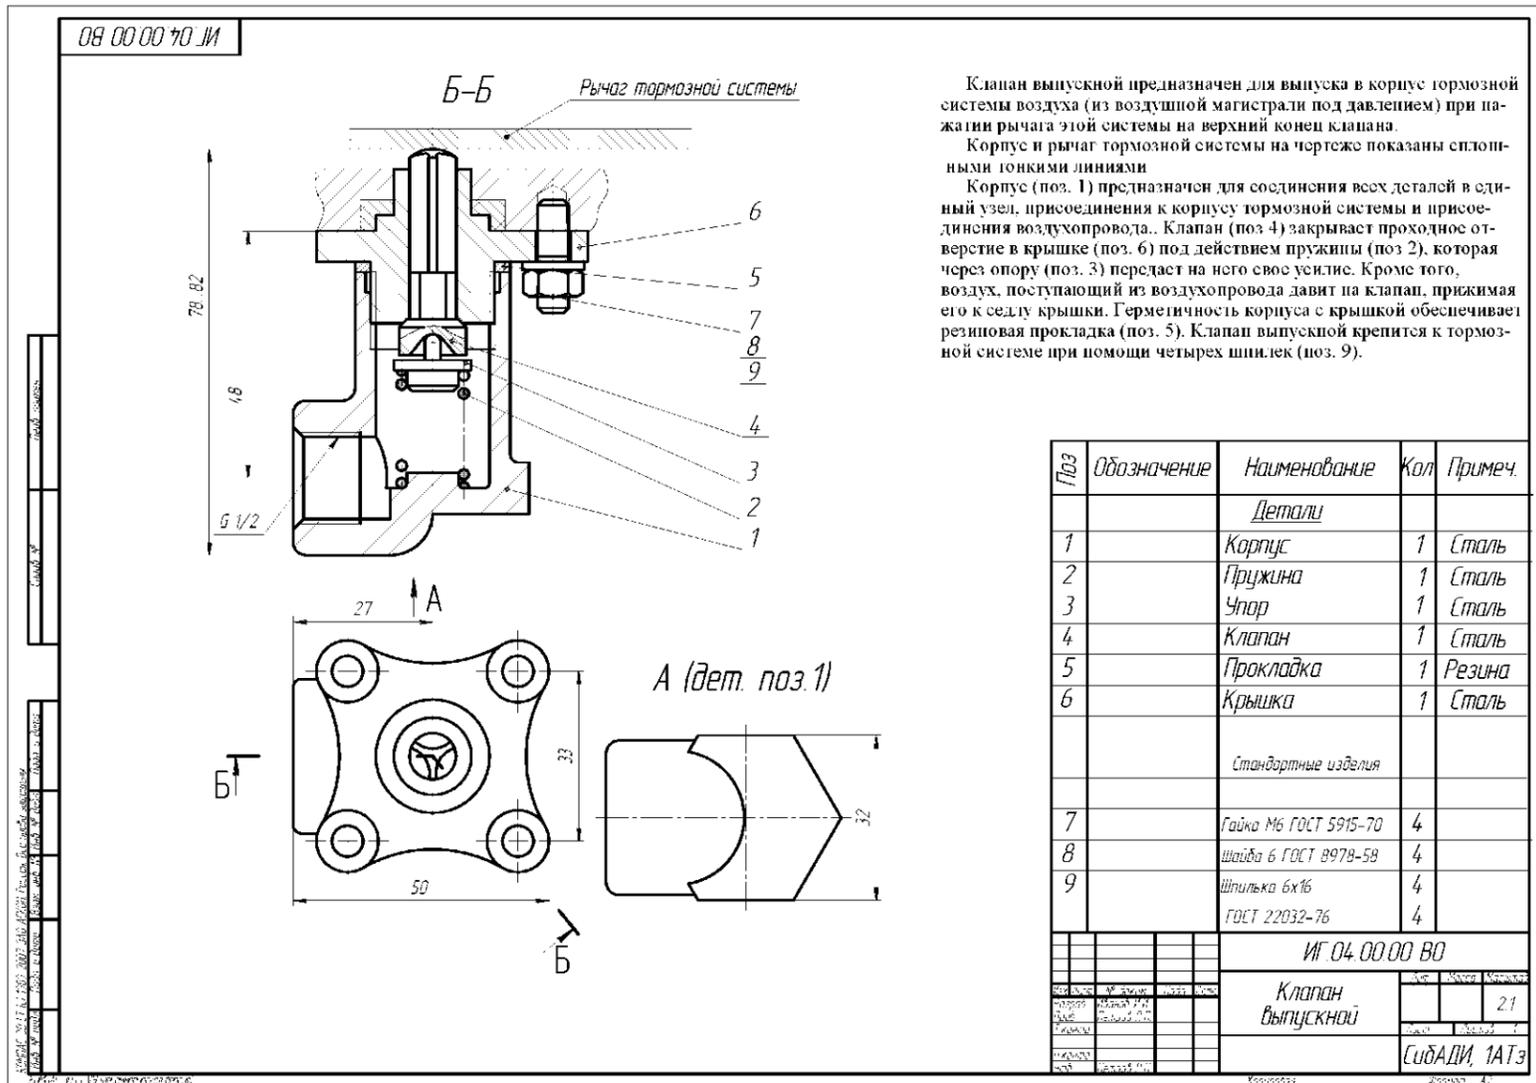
Чертеж общего вида сборочной единицы «Клапан выпускной»
